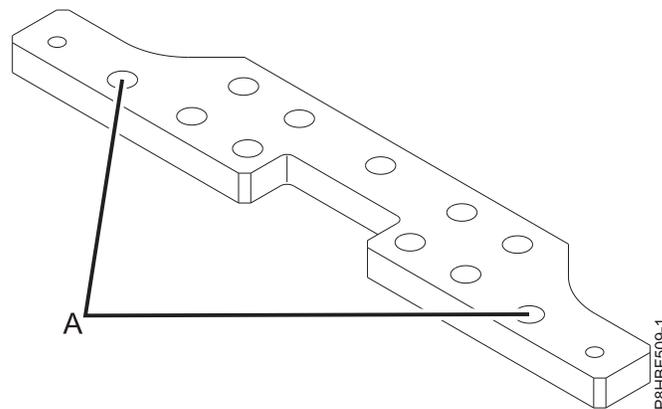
Localizações de furos da placa do parafuso inferior para rack com a chave triangular
